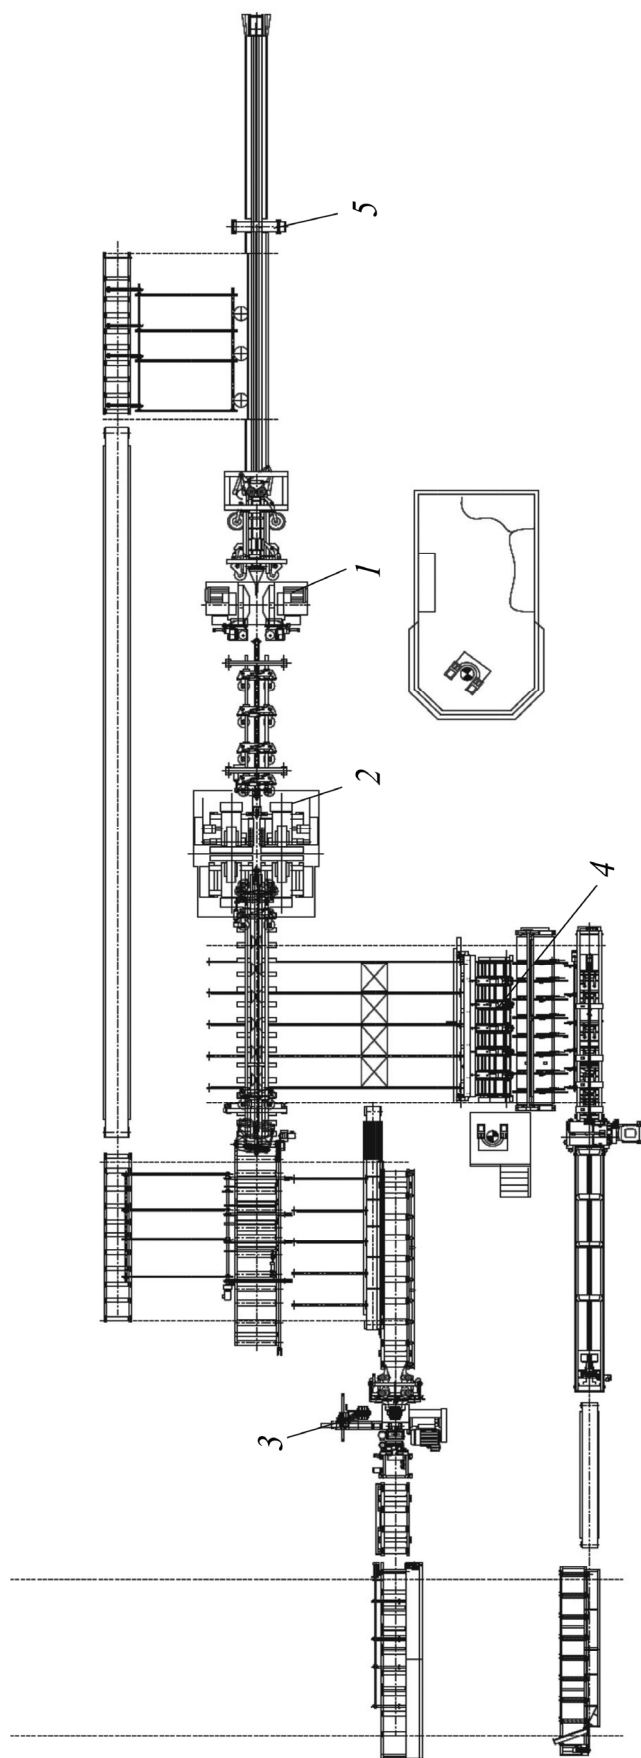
Схема лесопильной линии на базе фрезерно-ленточнопильного оборудования и делительного станка для бруса:
